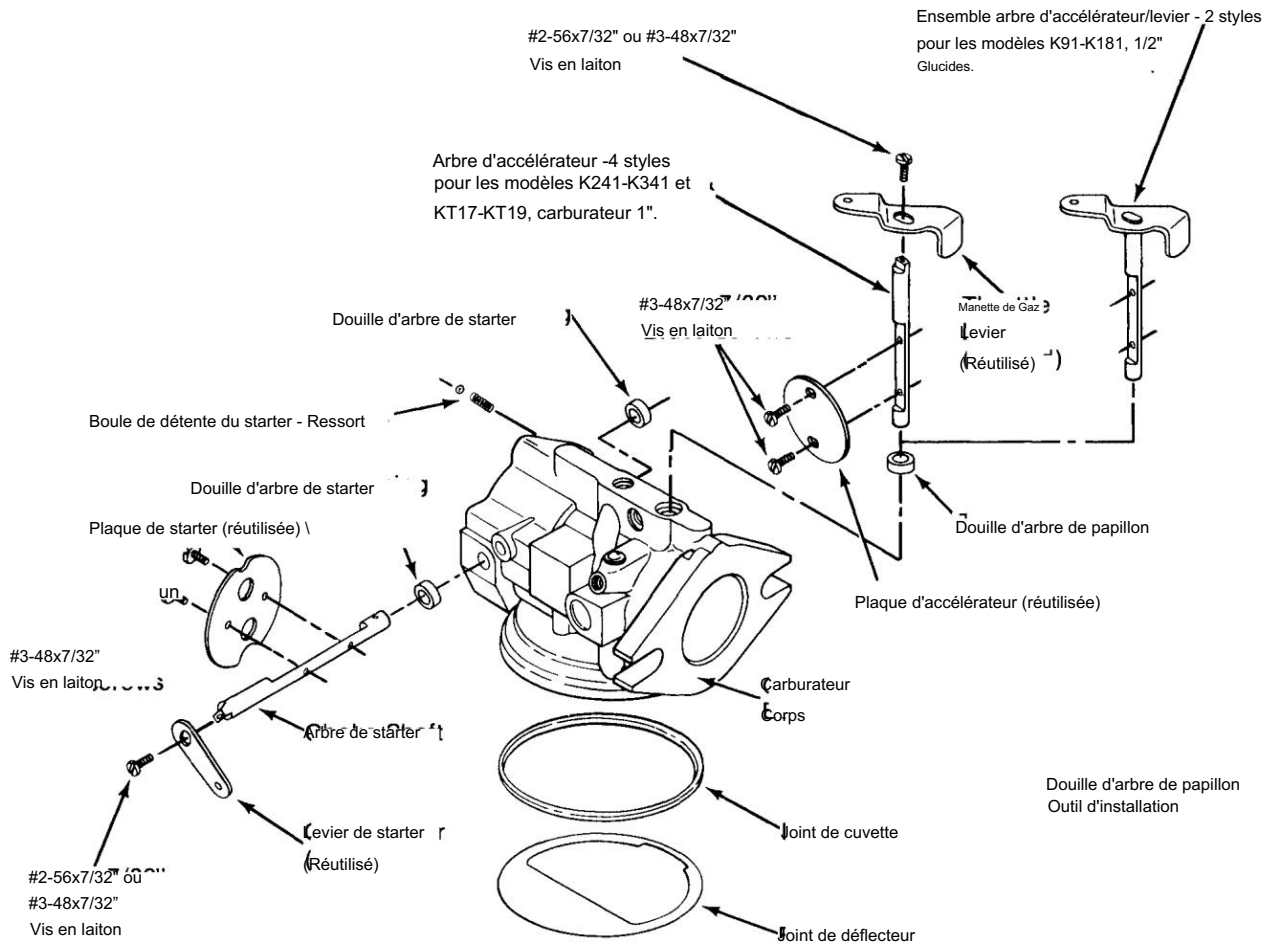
Kits de remplacement d'arbre d'accélérateur et de starter.
